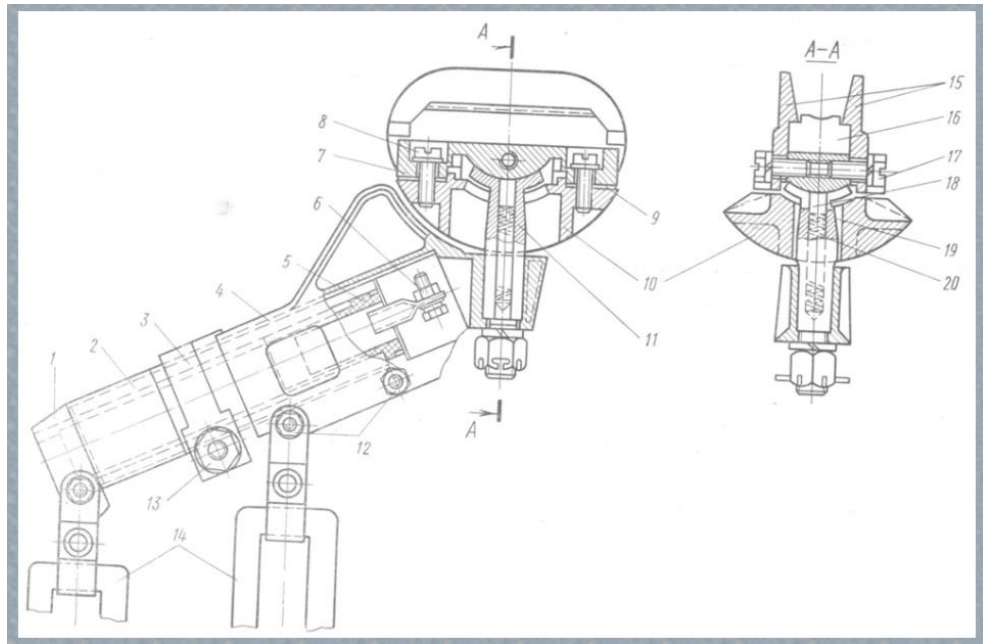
Головка ГТ-14А струмоприймача типу РТ-6І
